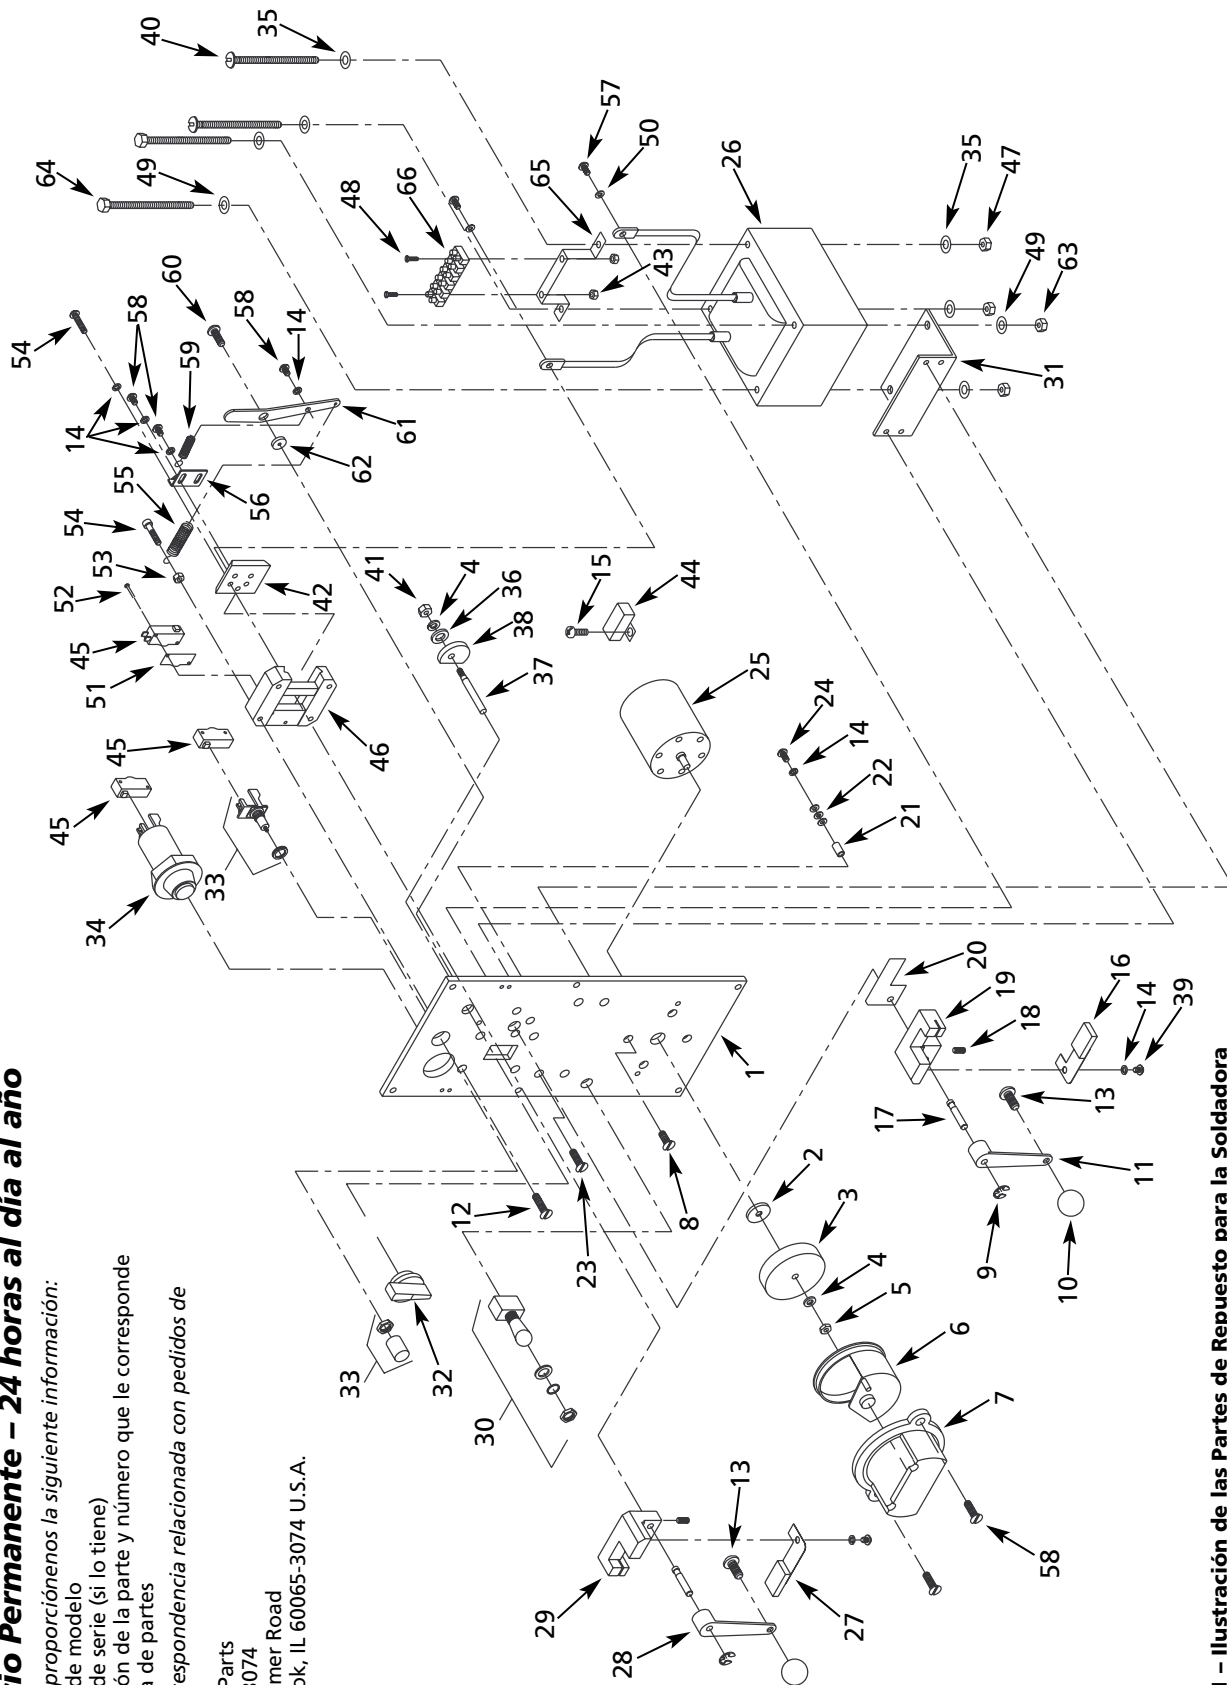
Ilustración de las Partes de Repuesto para la Soldadora
